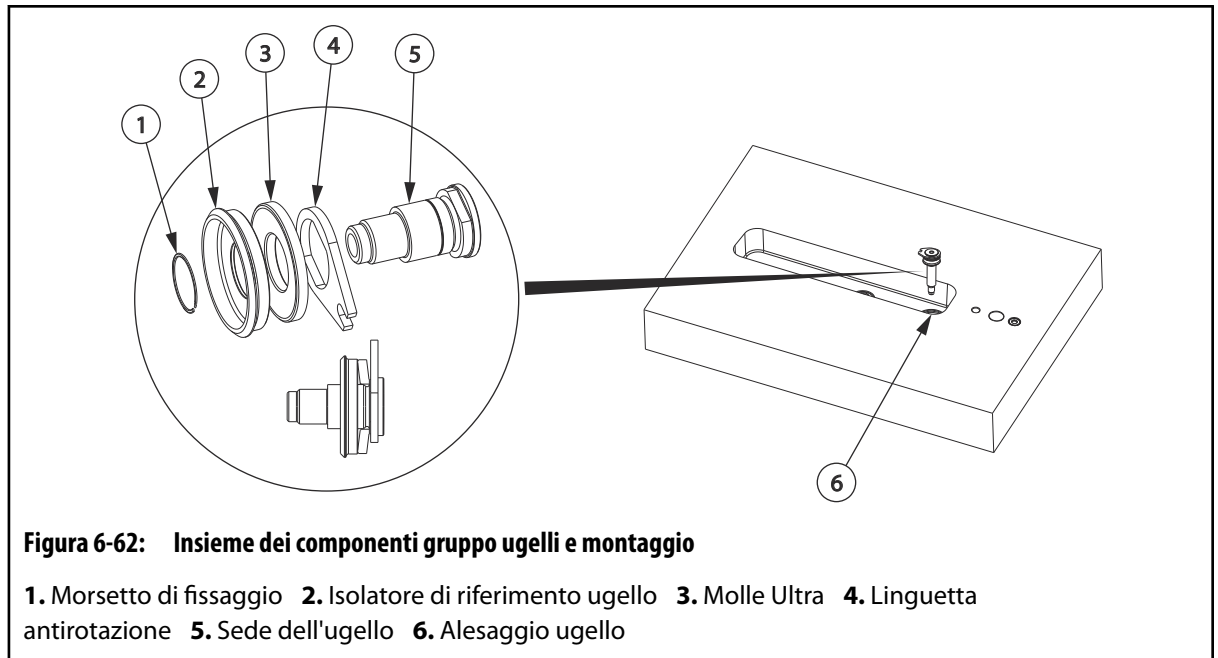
Insieme dei componenti gruppo ugelli e montaggio
